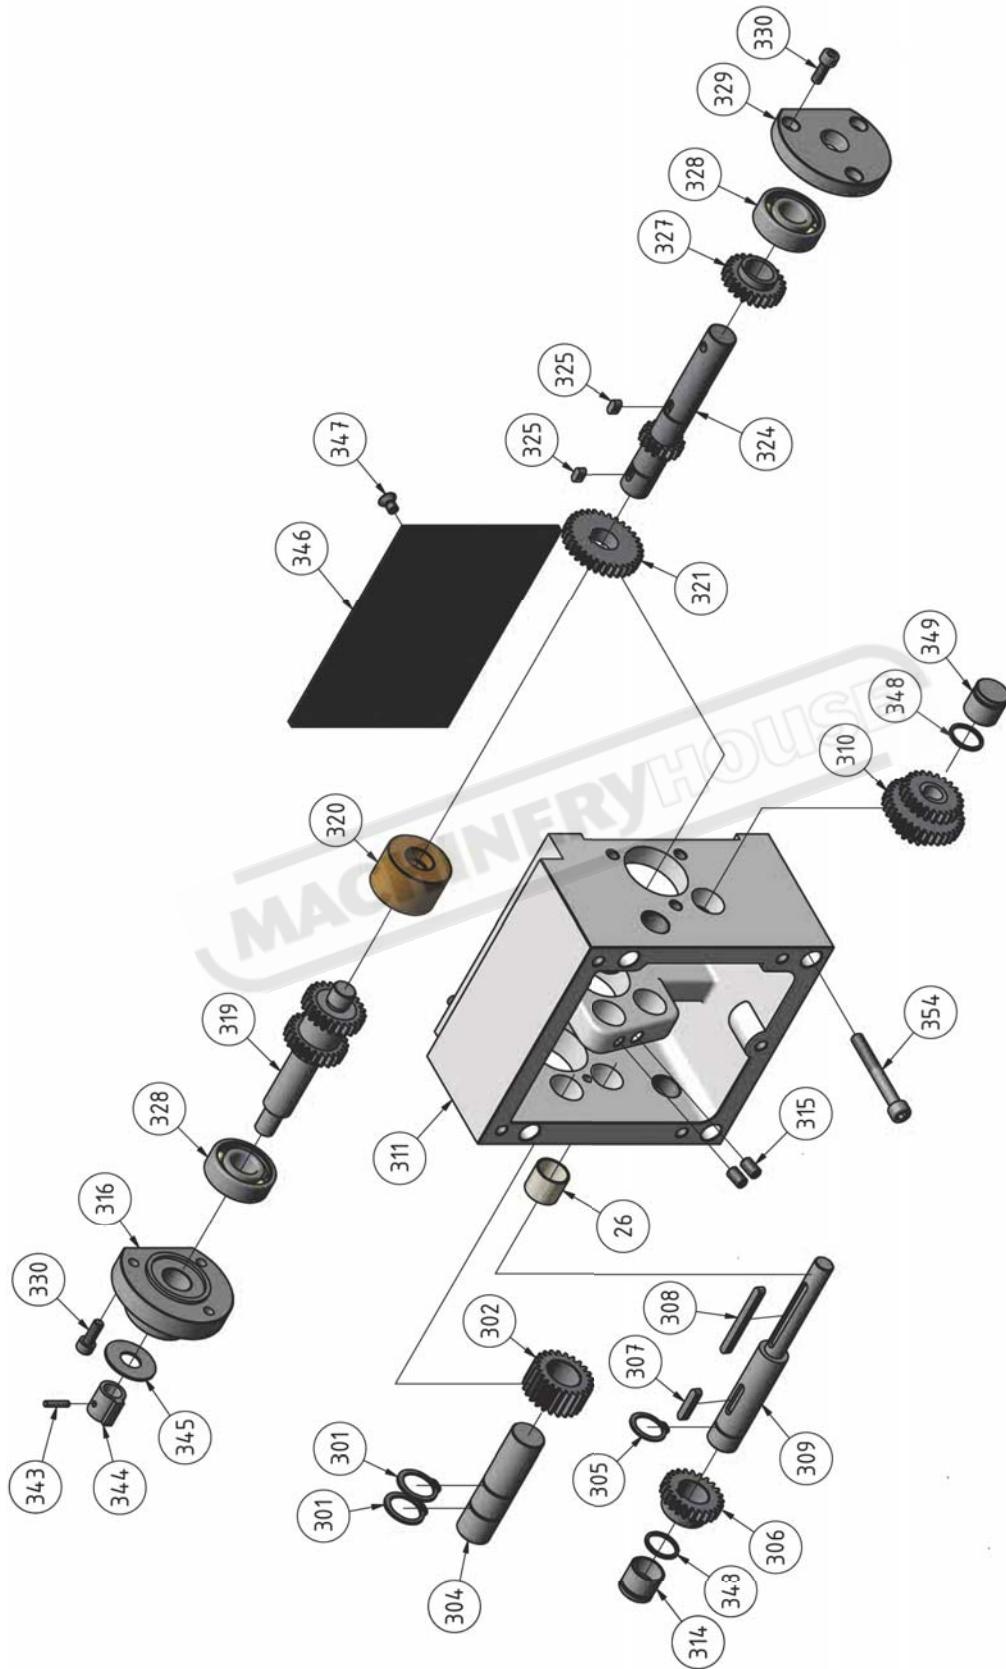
Vorschubgetriebe 2 von 2 - Feed gear 2 of 2 - TU2506
